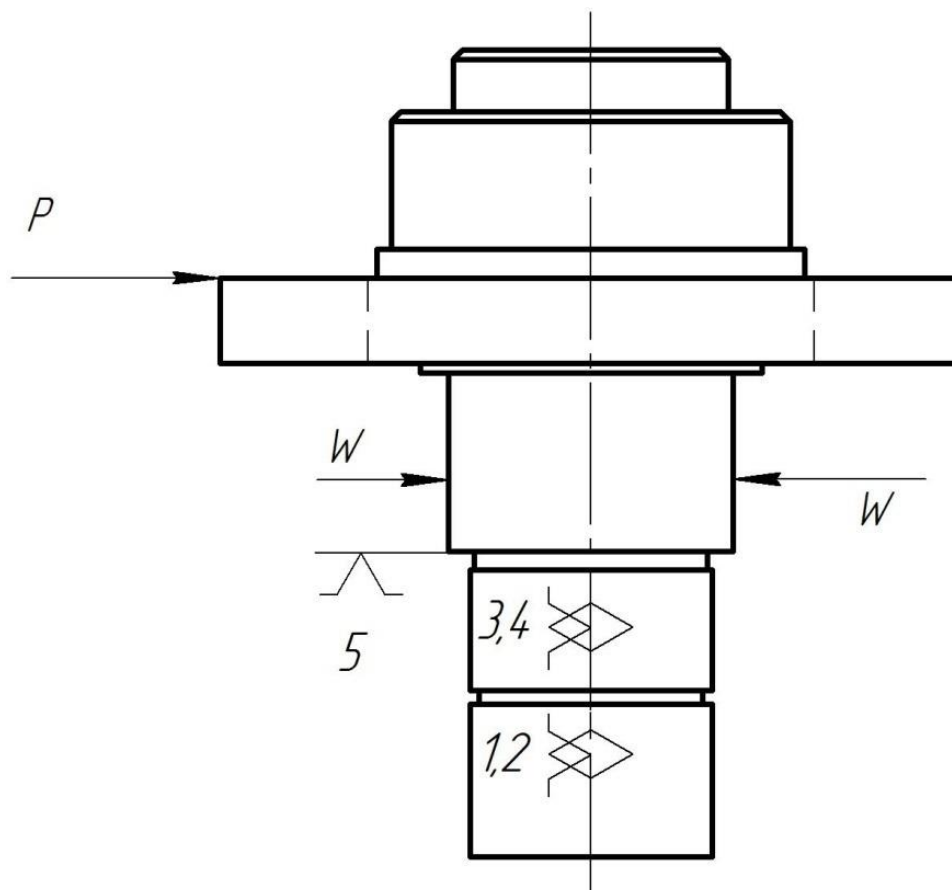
Схема базирования заготовки в приспособлении с указанием мест приложения силы зажима.
